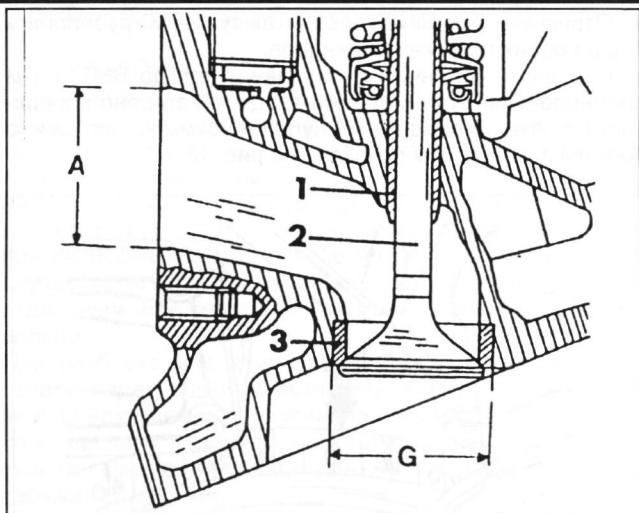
Разрез головки цилиндров. Размеры "А" и "G" различны для двух двигателей. 1 - направляющая втулка клапана, 2 - клапан, 3 - седло клапана.
